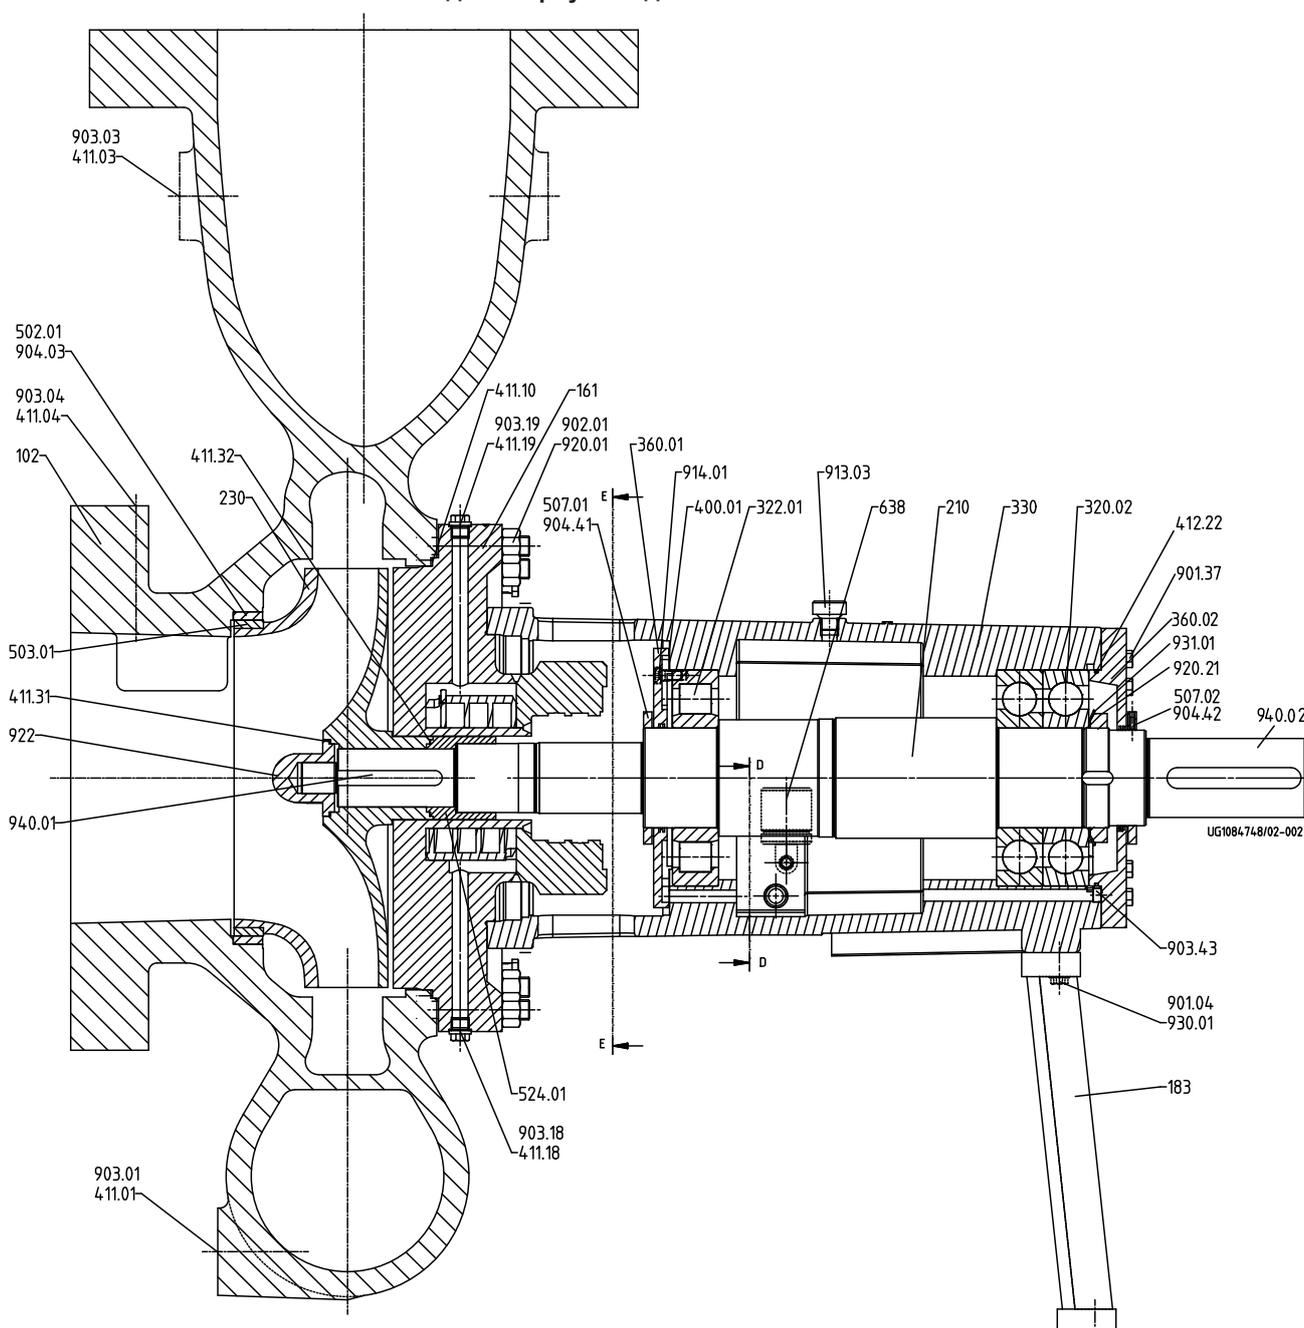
Сборочный чертеж исполнения с подшипниковым кронштейном В07
